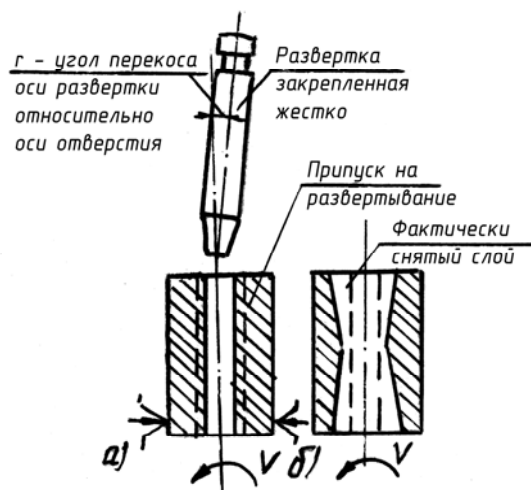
Разбивка отверстия при жестком креплении развертки: а) заготовка до развертывания б) после развертывания
